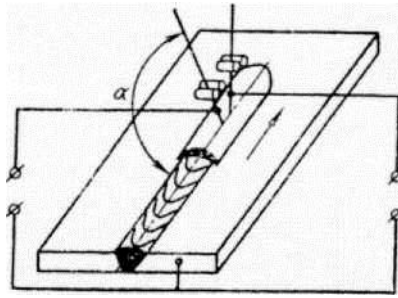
Схема утворення шва при дводуговому зварюванні
